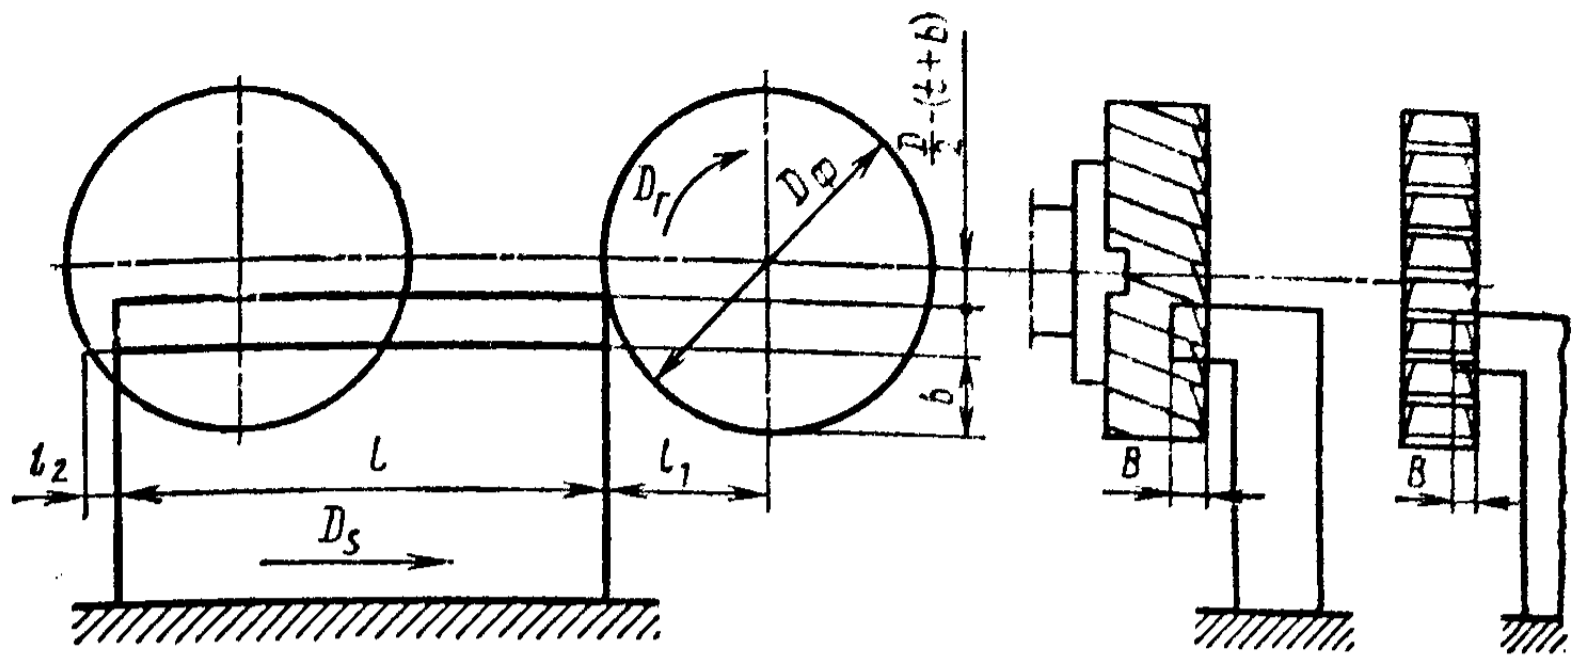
Путь, пройденный инструментом при несимметричном фрезеровании торцовыми и дисковыми фрезами
